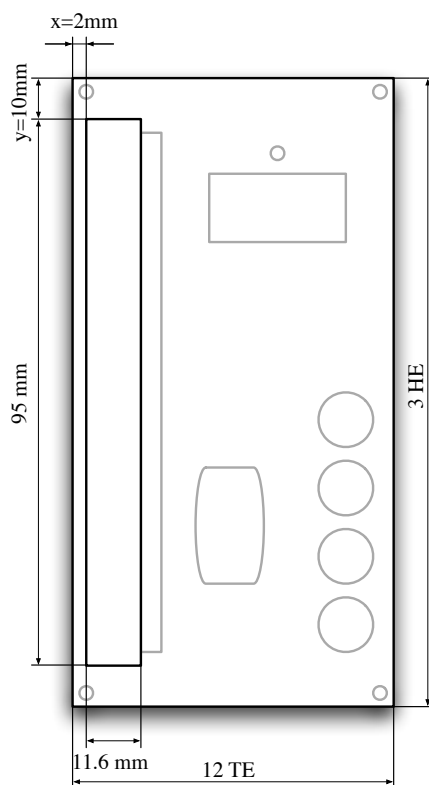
CAD Zeichnung des 19-Zoll Frontblechs des Mainboards.
